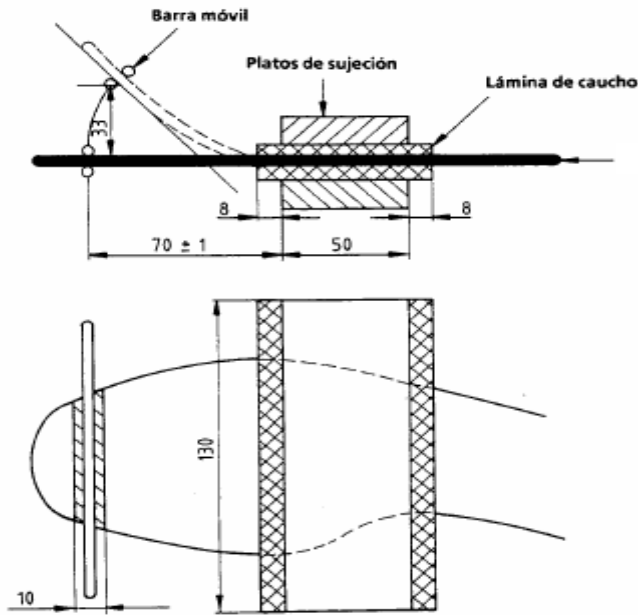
Equipo de flexión para plantillas de protección (medidas en mm)
